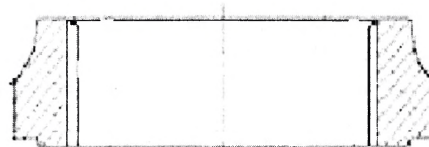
Фрагмент внутренней цилиндрической части детали ступица шестерни
